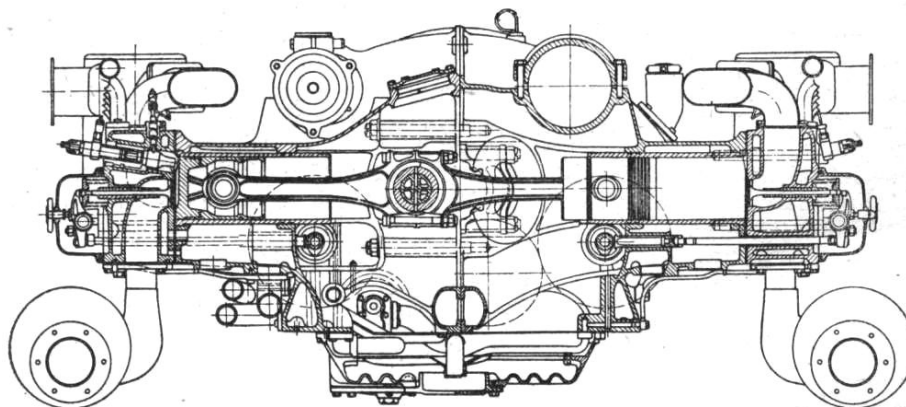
Secțiune printr-un motor Diesel cu cilindri orizontali
